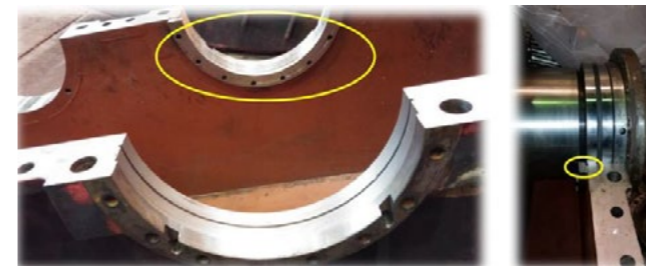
Gövdede Flanşın Oturacağı Yerin İşlenmesi
